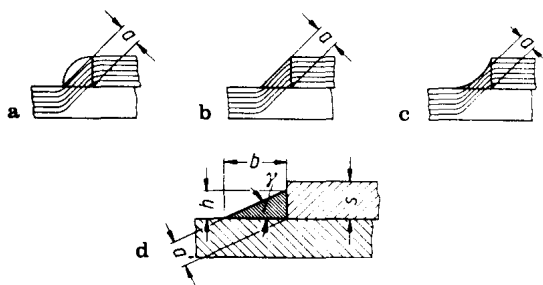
焊缝形式和力流 a.凸型; b.平型; c.凹型; d.不对称型角焊缝
